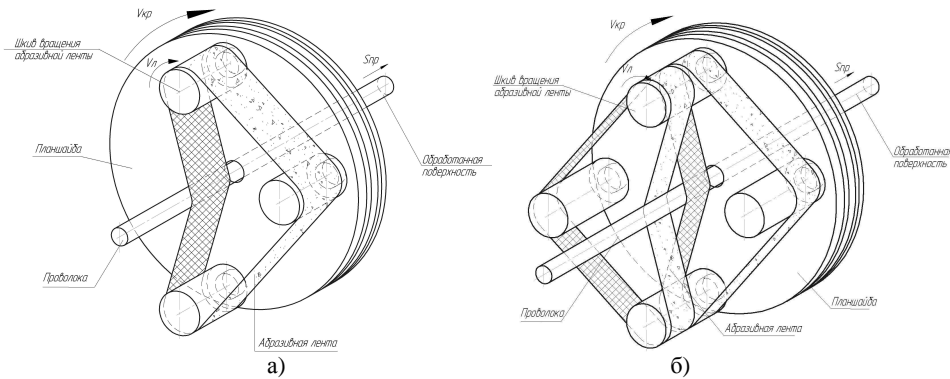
Схема ротационного ленточного охватывающего шлифования: а) с одной абразивной лентой; б) с двумя абразивными лентами
